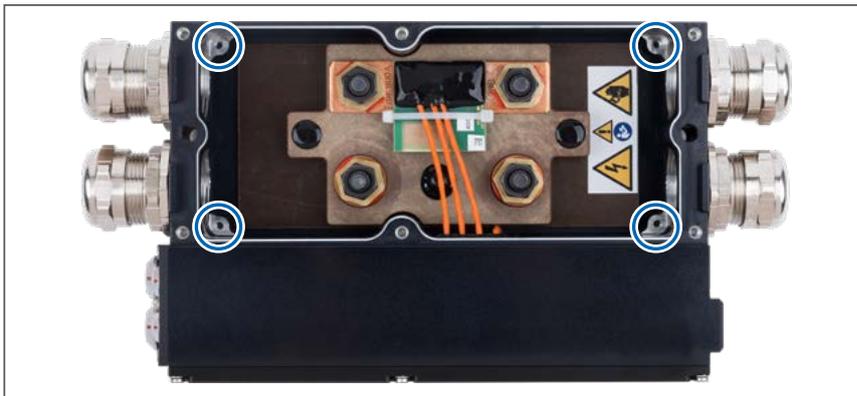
HV BM 1.2, Gehäuse offen und M3-Gewindebohrungen markiert
